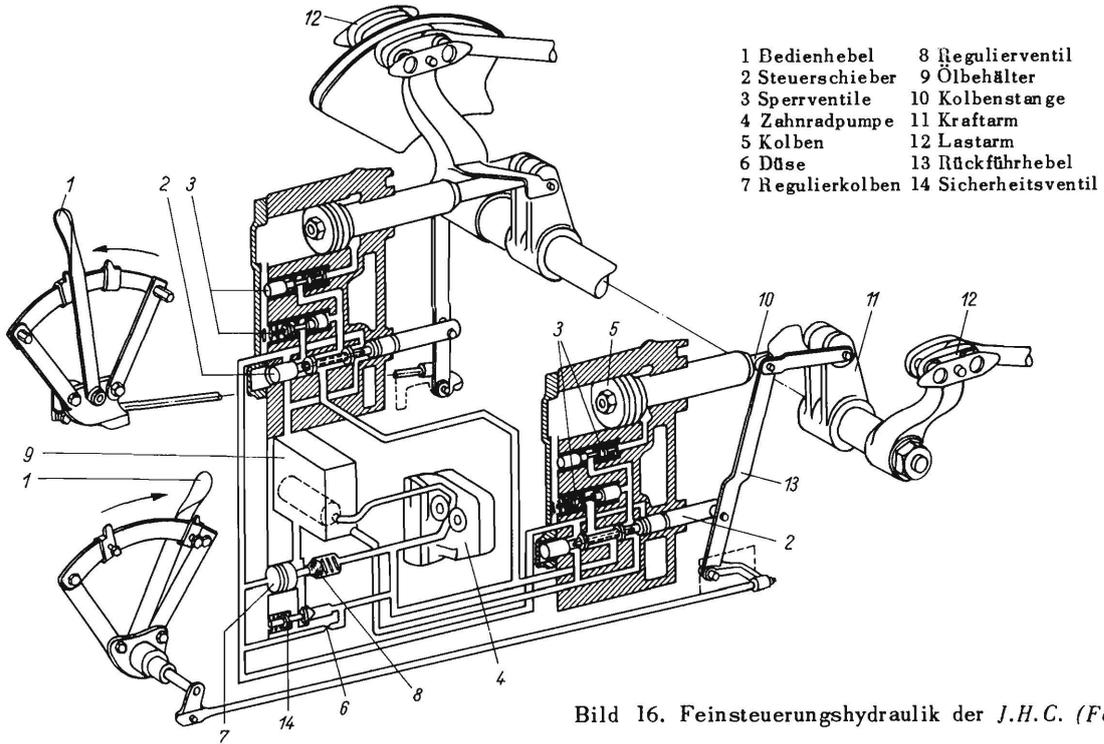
Feinsteuerungshydraulik der J.H.C. (Farmall A)
